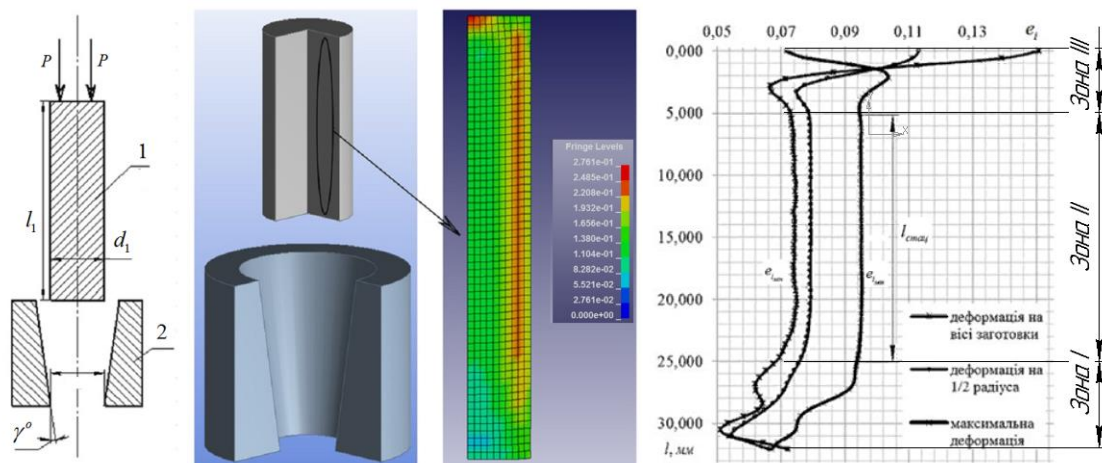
Редукування заготовки (1 – заготовка, 2-матриця)
